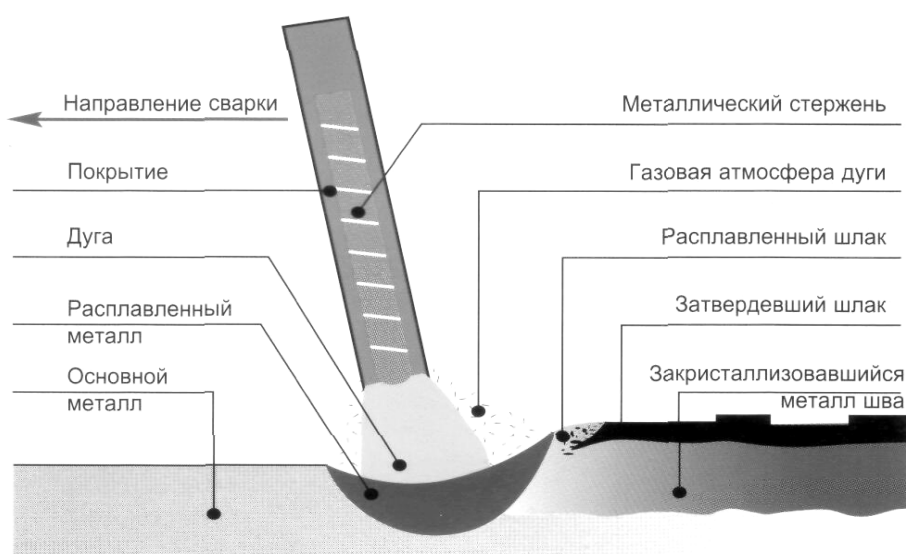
Ручная дуговая сварка металлическим электродом с покрытием.
